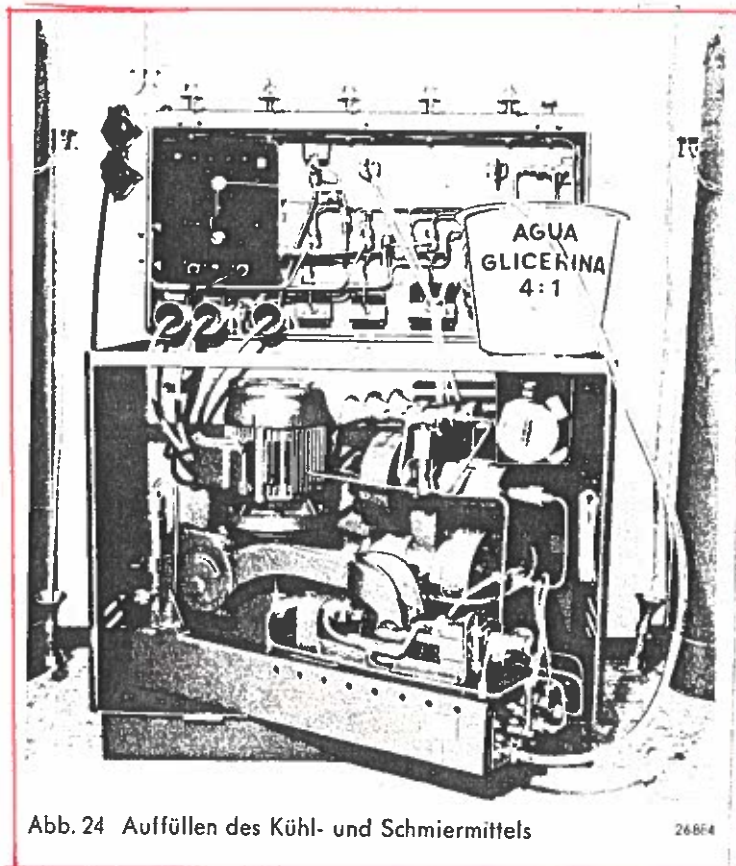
Auffüllen des Kühl- und Schmiermittels
